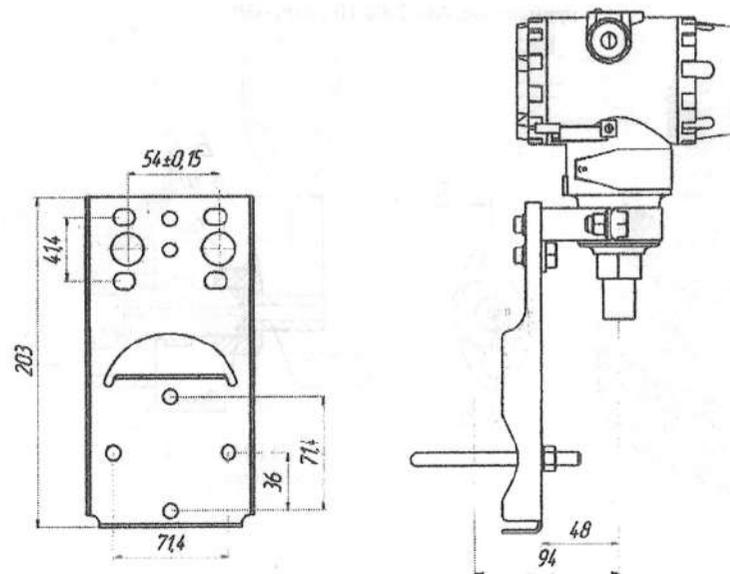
Кронштейн для крепления на трубе, габаритные и присоединительные размеры: В14 – для исполнений 4-6, В17 – для исполнений 7-0
